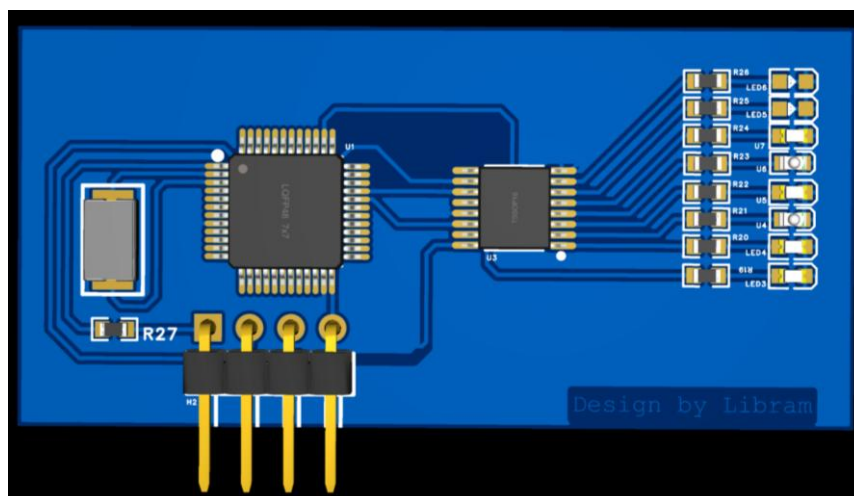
8 位流水灯 PCB 顶层 3D 外壳预览图
